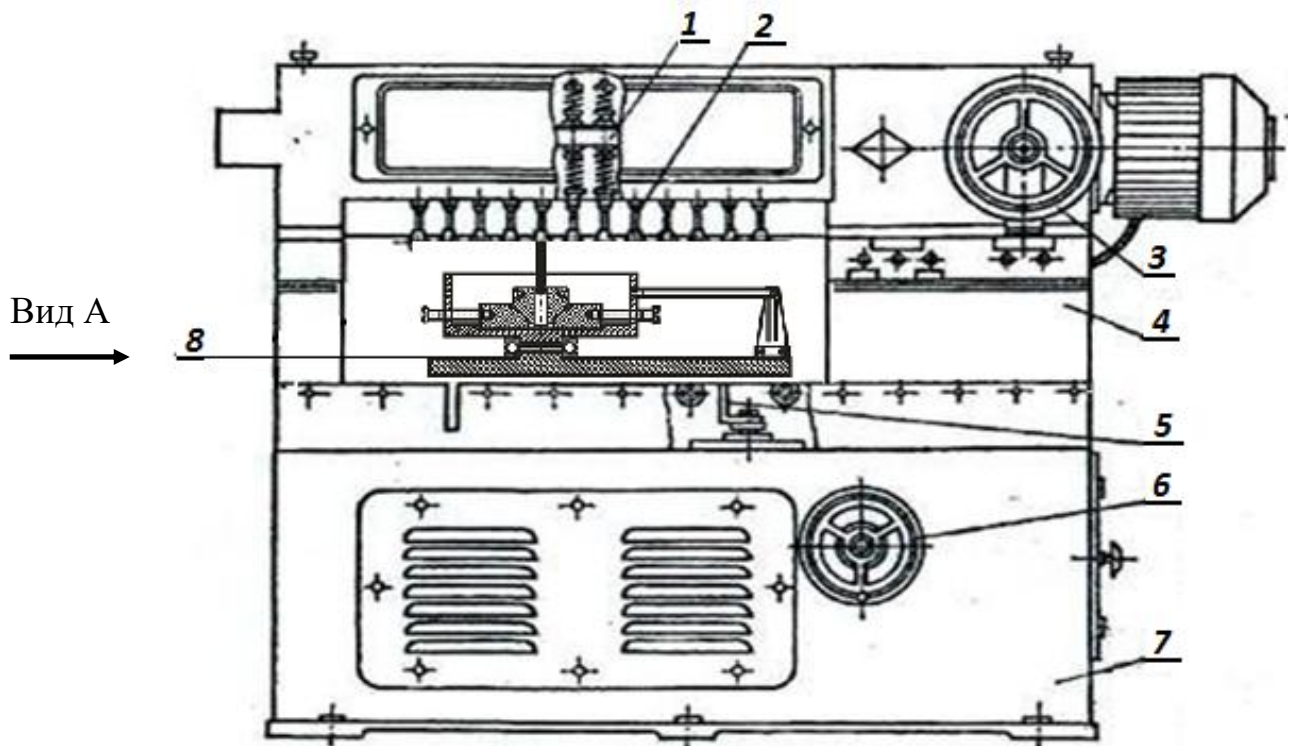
Лабораторна установка для дослідження працездатності притирального складу [5]: 1 – блок шпинделів; 2 – перехідник; 3, 6 – маховик; 4 – стійка права; 5 – косинець підйомного столу; 7 – станина; 8 – робочий вузол для притирання
